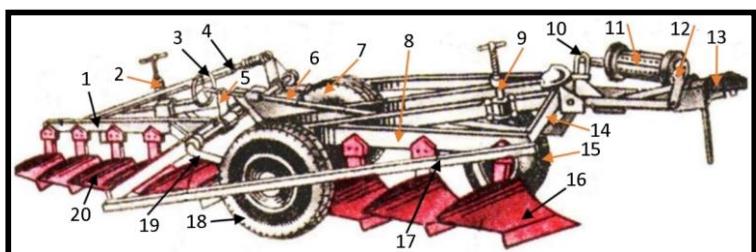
Общий вид лущильника лемешного ППЛ-10-25: 1 – главный брус секции задней; 2 – регулятор колеса задней секции; 3 – штурвал управления опорным колесом; 4 – догружатель задней секции пружинный; 5 – рычаг; 6 – тяга; 7 – колесо опорно-регулировочное; 8 – главный брус рамы секции передней; 9 – механизм регулировочный колеса секции передней; 10 – рычаг; 11 – гидроцилиндр; 12 – гидроцилиндр; 13 – прицеп; 14 – рама главная; 15 – колесо переднее опорно-регулировочное; 16 - корпус передней секции; 17 – растяжка рамы; 18 – колесо опорно-транспортное; 19 – П-образная ось; 20 – корпус задней секции.
